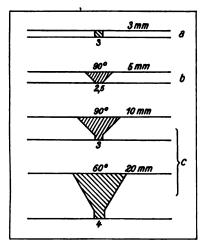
Beispiele normaler Blechschweißungen.
